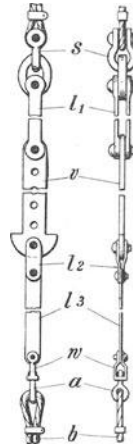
2) Unterseilgehänge mit Ausgleichvorrichtung für Seillängen.
